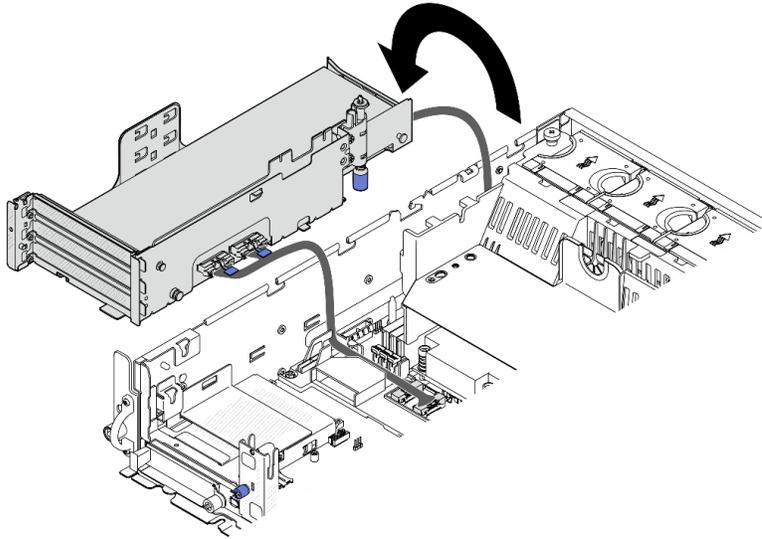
Colocar la expansión PCIe 1 a un lado del chasis
